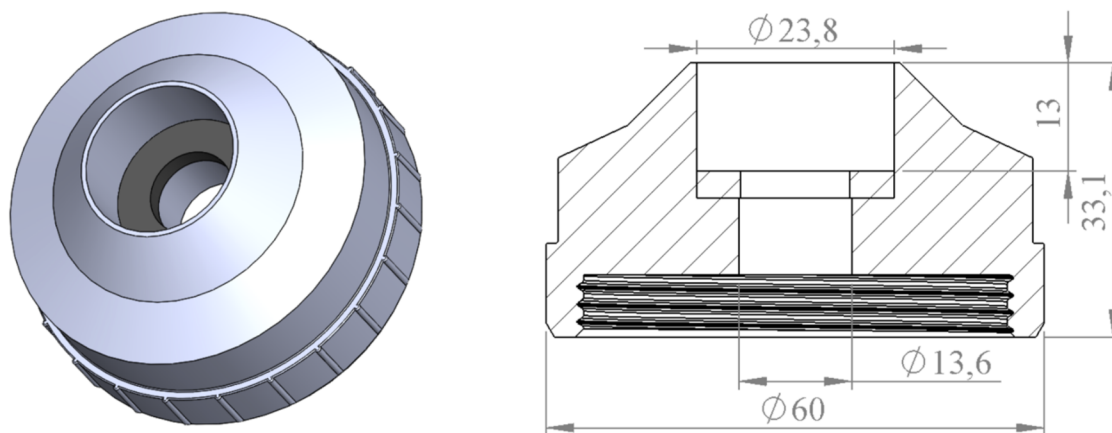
Připojení závěsného sluchadla k akustické spojce [16].
